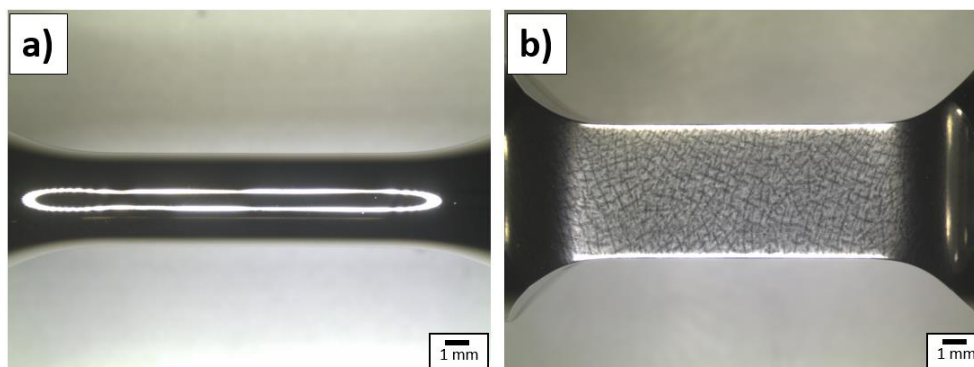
Etat de surface après préparation des 2 types d'éprouvette. a) Eprouvette cylindrique après polissage 1  $\mu\text{m}$ . b) Eprouvette à section carrée après polissage électrolytique.
